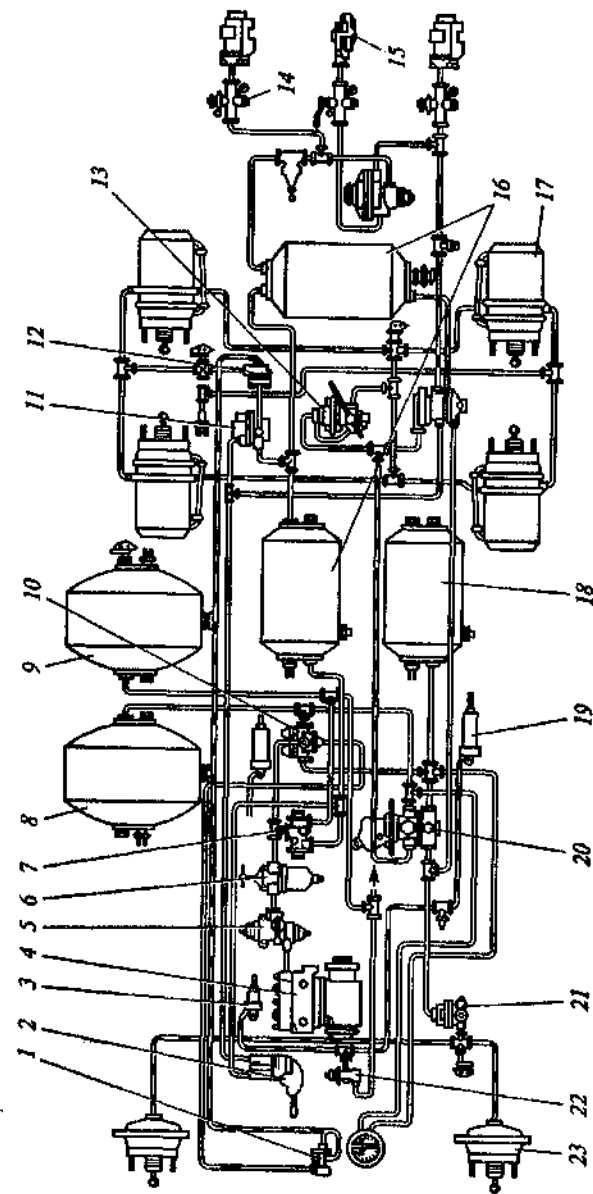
Пневматический тормозной привод грузового автомобиля КамАЗ:
